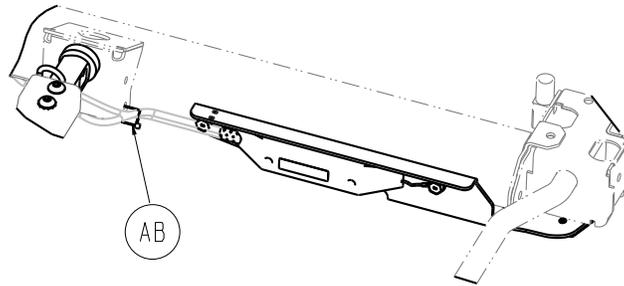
Emplacement du collier de serrage - ensemble IR/appel infirmier
